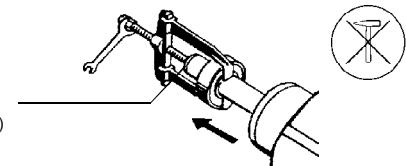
Lagerwechsel / Changing bearings / Remplacement des roulements
